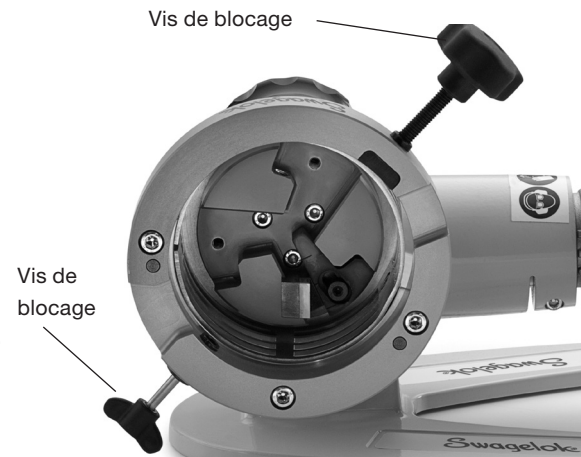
Insertion et remplacement des coquilles de blocage TF48
